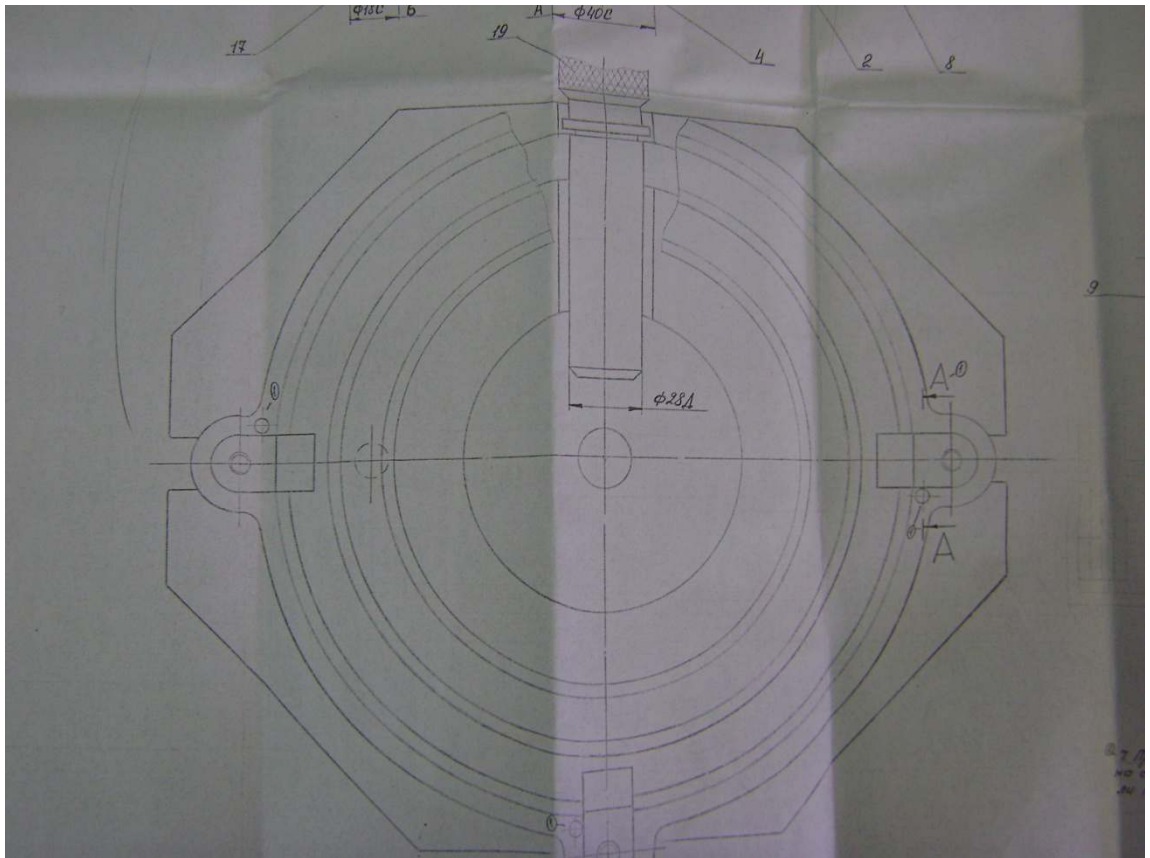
Фрезерное приспособление ВУ7210 – 6273
